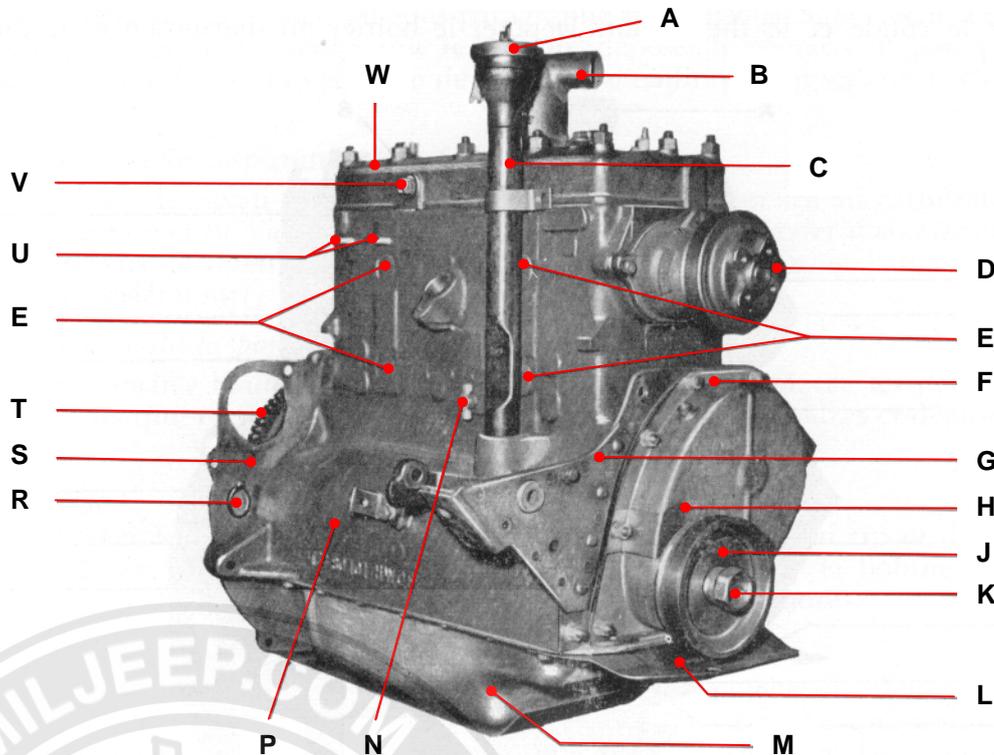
Vue de trois-quarts avant gauche du moteur déshabillé.
